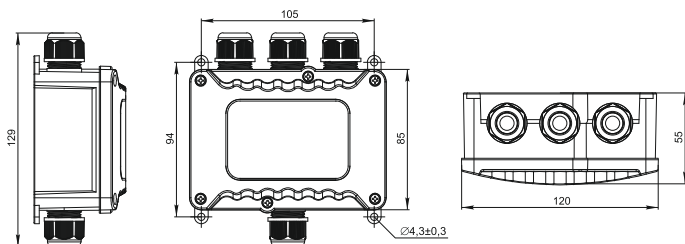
Габаритные размеры коробки WTP-404 / Figure 4 – Overall dimensions of the WTP-404 box
